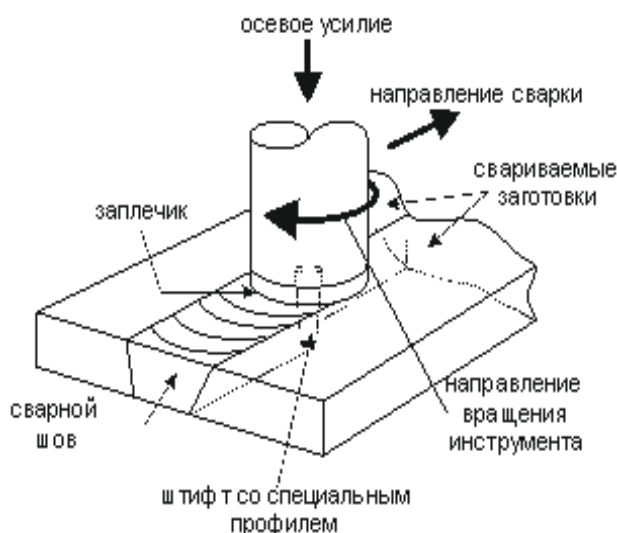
Схема процесса сварки трением с перемешиванием [1]
